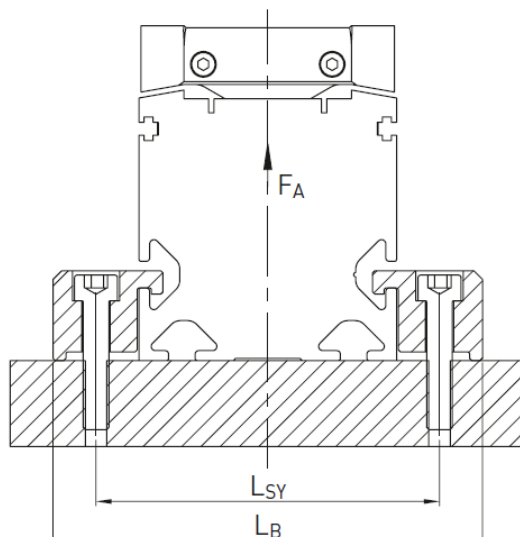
Befestigung mit Spannprofilen – HM040S, HM060S, HM080S
